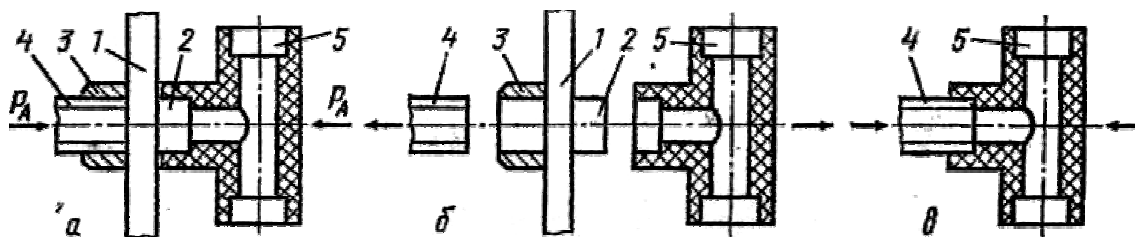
Принцип сварки в раструб фитингов и втулок: а — подогрев свариваемых деталей; б — отвод нагретого инструмента; в — состыковка (сварка); 1 — нагретый инструмент; 2 — нагретый (сварочный) дорн; 3 — нагретая (сварочная) гильза; 4 — пластмассовая труба; 5 — пластмассовый фитинг
